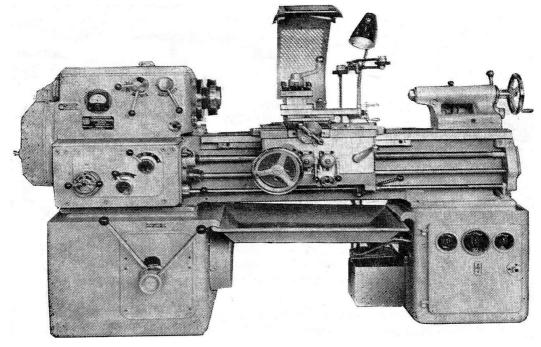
Токарно-винторезный станок модели 1А616П
